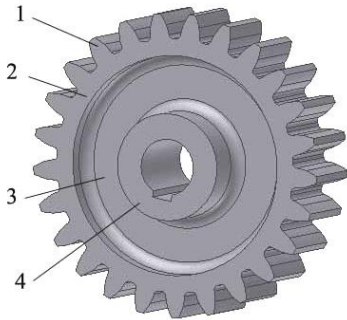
Конструктивні елементи циліндричного зубчастого колеса
